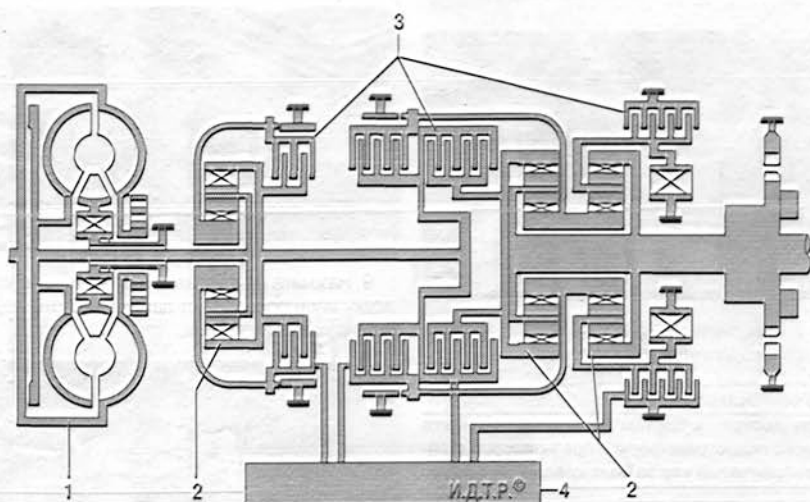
Кинематическая схема автоматической коробки передач: 1 – гидротрансформатор; 2 – планетарный ряд; 3 – фрикционные блоки; 4 – исполнительный механизм
